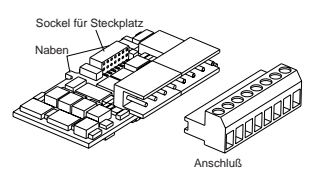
Entfernen Sie den Steckverbinder, bevor Sie das Eingang-2-3-Modul installieren.
